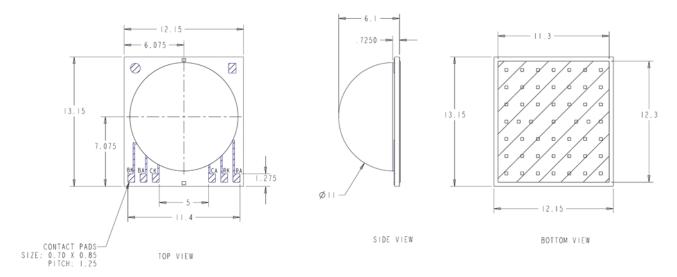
Габаритный чертеж корпуса светодиода MP-L EZW
